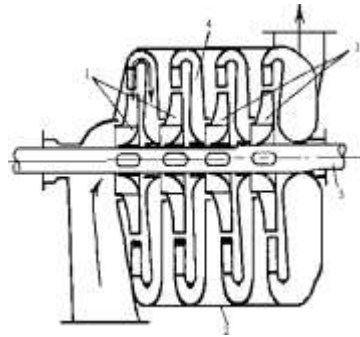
Схема багатоступінчастого насоса: 1 – робоче колесо; 2 – корпус; 3 – вал; 4 – відвідний канал
